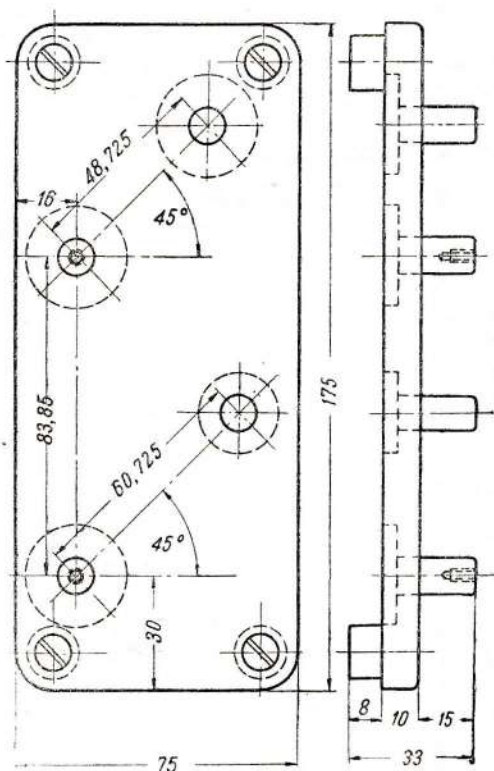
Прибор для проверки сцепления шестерен ТОМП-4 (дет. № 21, 22а, 23, 24). Для осей использовать оси Т-4 (дет. № 76, 77, 78)
